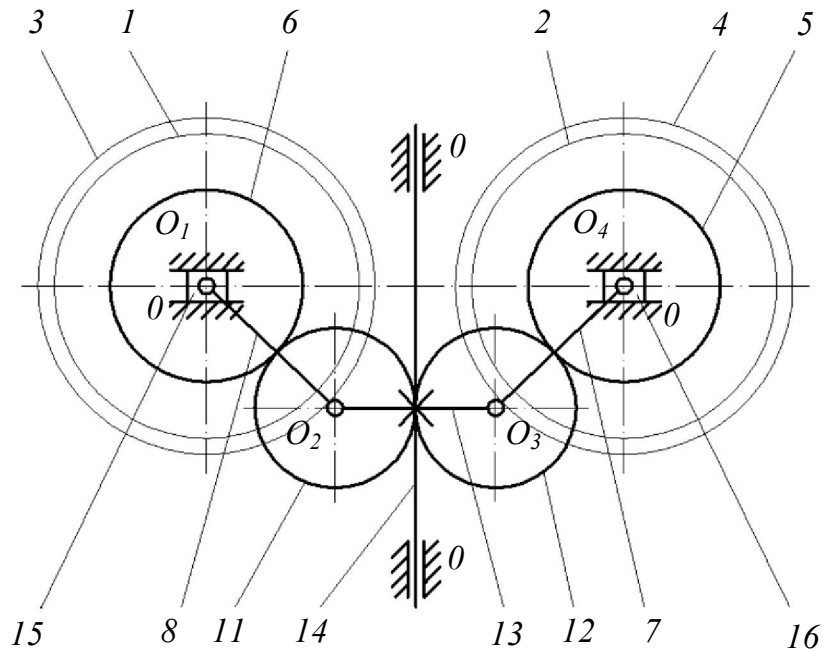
Первый вариант новой конструкции механизма привода валковой пары
